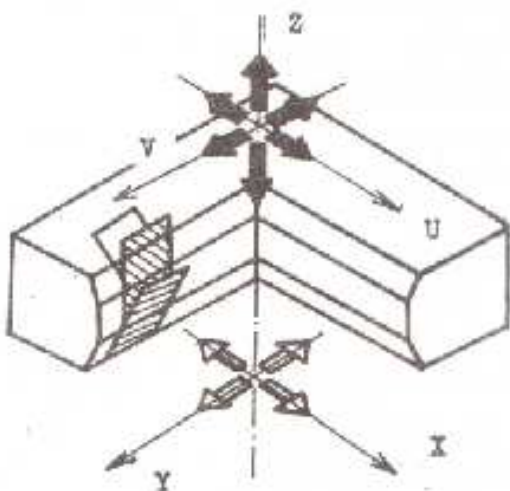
Schéma vedení a podávání drátové elektrody [8]
